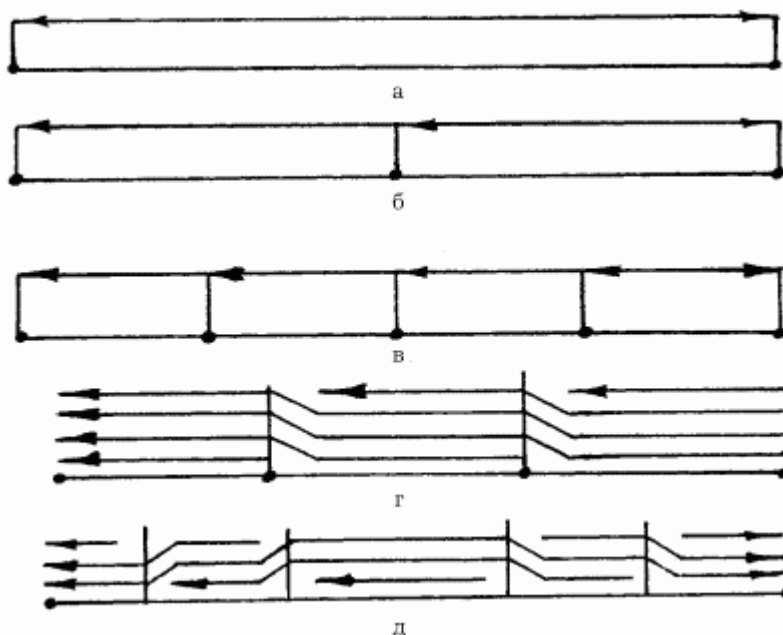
Различные схемы сварки: а – сварка напроход; б – сварка от середины к краям; в – обратноступенчатый способ; г – «каскад»; д – «горка».
